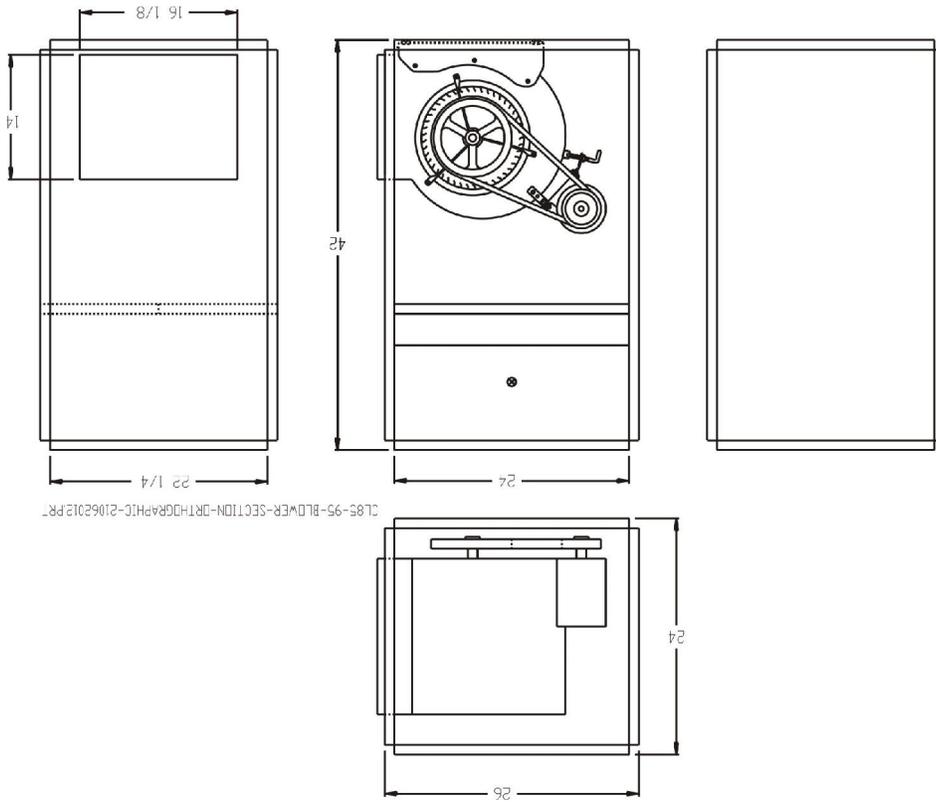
DIMENSIONS HORS TOUT DU BLOC VENTILATEUR OPTIONNEL
